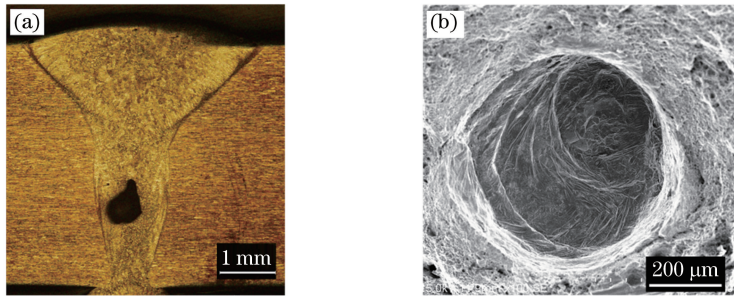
焊缝气孔。(a) 宏观特征;(b) 内部形貌
